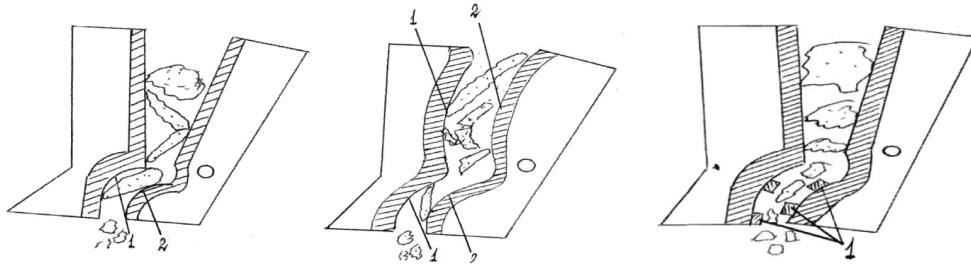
Принципиальные схемы щековых дробилок для дробления «плоскушки»: 1 – углубление на неподвижной щеке, 2 - выступ на подвижной щеке
